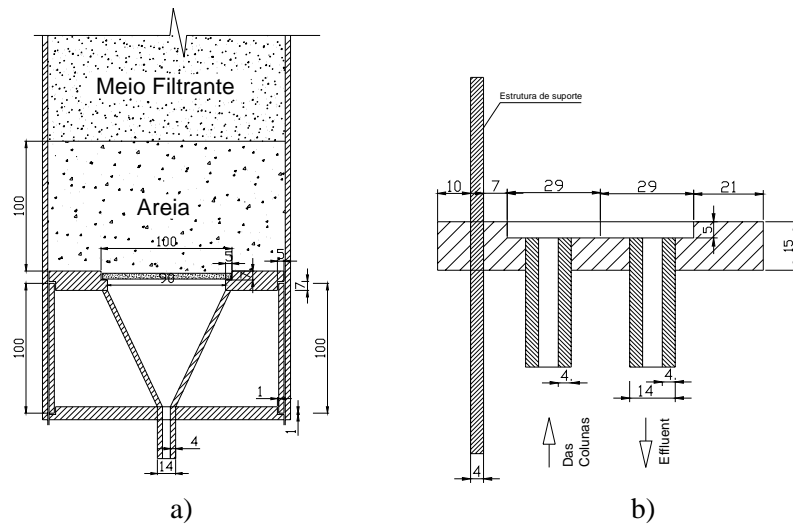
Pormenores das colunas (medidas em mm): a) Suporte inferior; b) Descarregador
